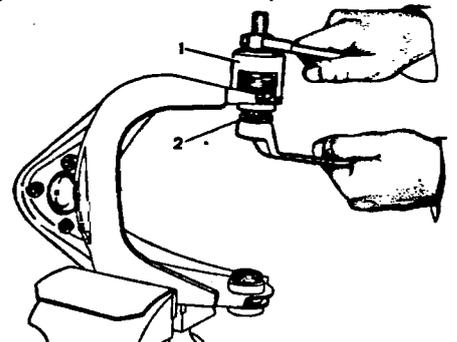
Выпрессовка шарниров верхнего рычага: 1 - приспособление А.47046; 2 - шарнир
